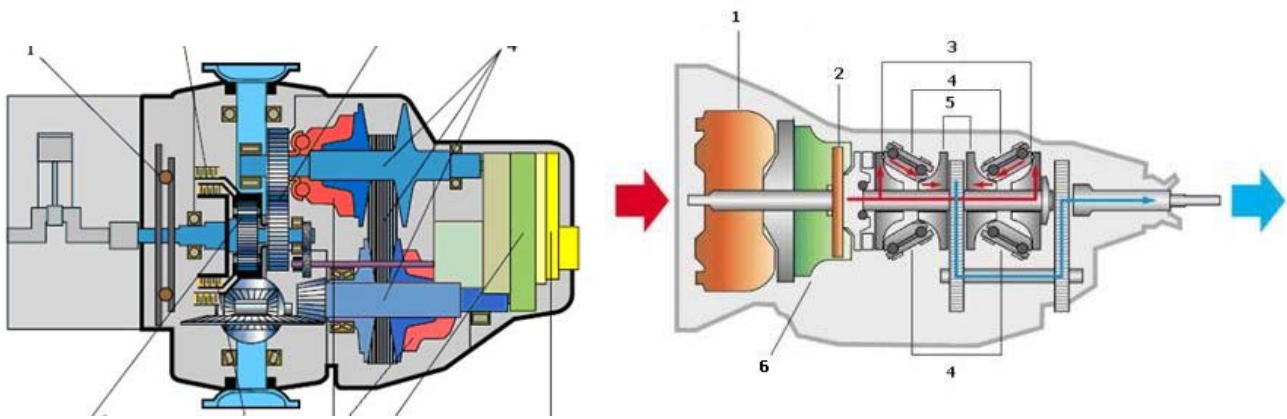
Коробки передач клиноремінні та тороїдні
